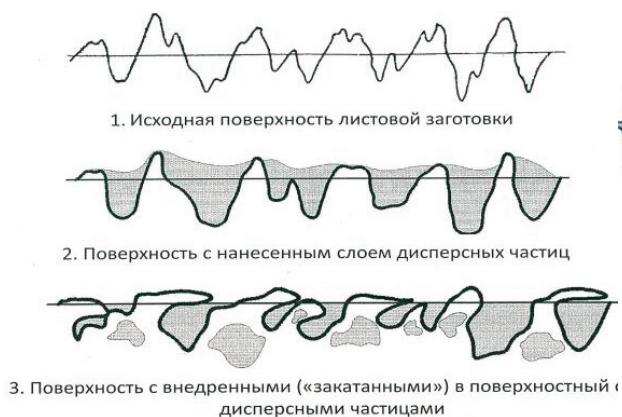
Схема обработки поверхностного слоя листовой заготовки
